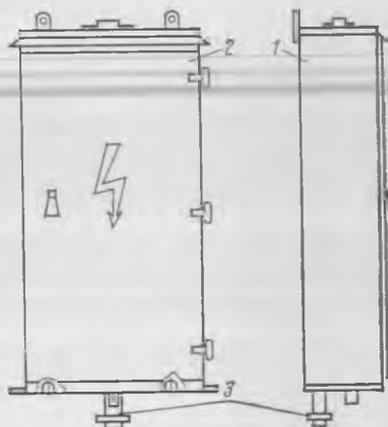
Шкаф кабельный междуродный (ШКМ): 1 — корпус; 2 — дверь; 3 — патрубок
